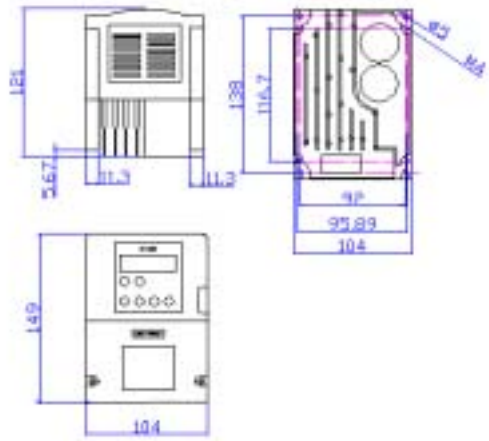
为200W ~ 1.5KW的外形尺寸及安装尺寸
